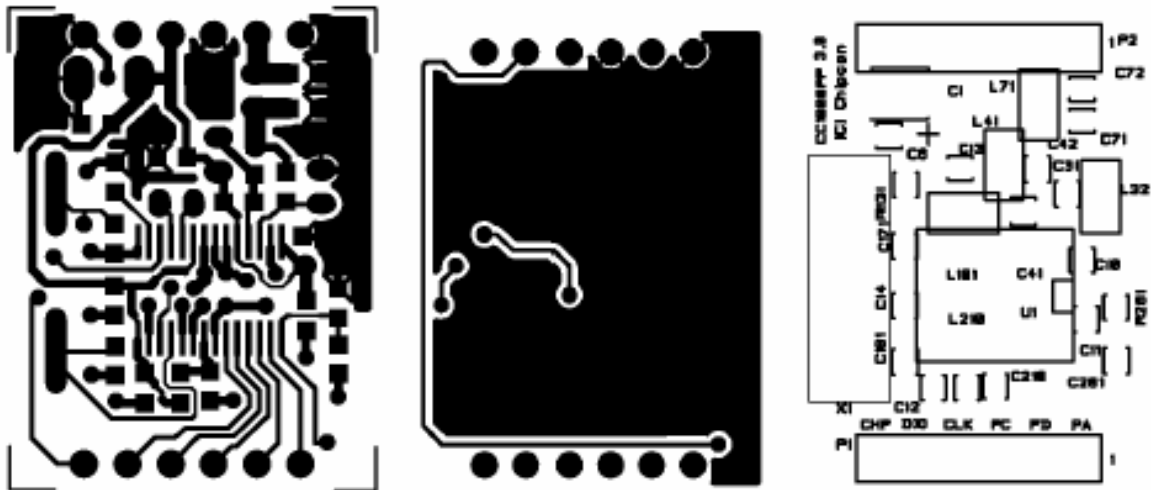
Parte superior e inferior del layout de la PCB y esquema de su diseño
